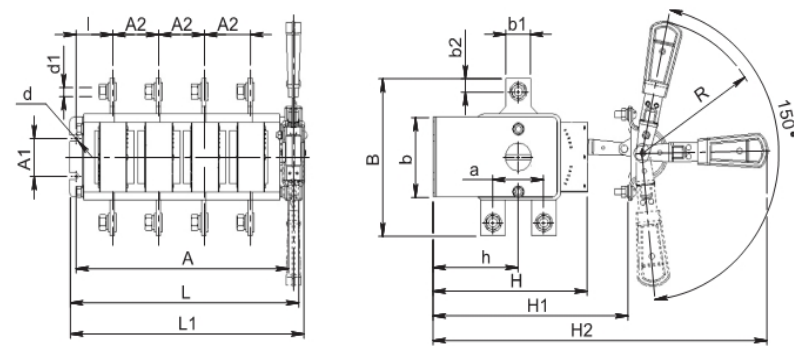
Б Выключатель-разъединитель на два направления 4-полюсный с передней смещенной рукояткой
